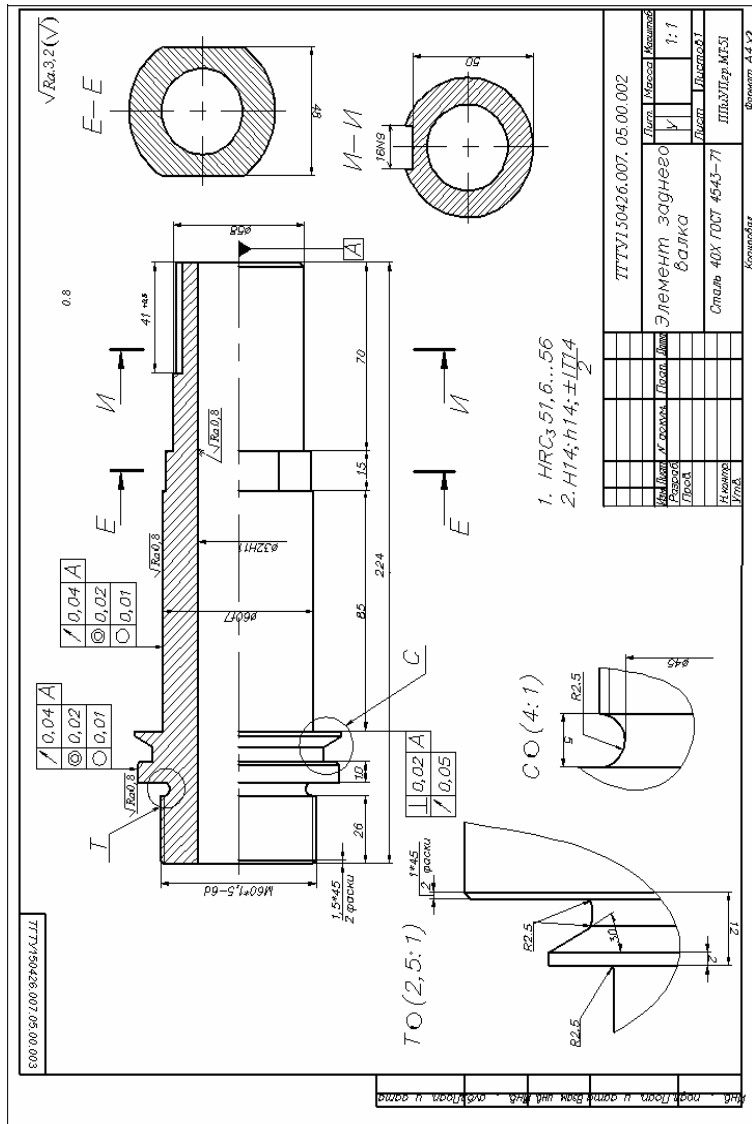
Рабочий чертеж правого элемента заднего вала вальцев
